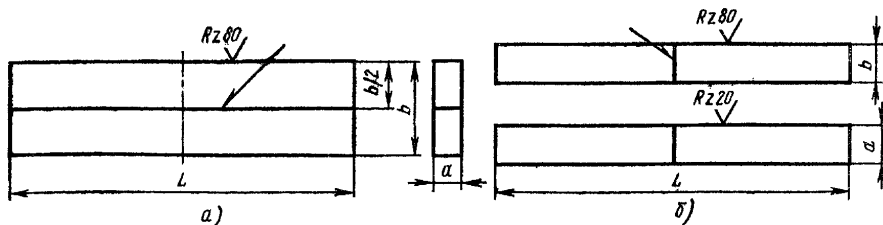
Образцы для испытания сварного соединения на статический изгиб
